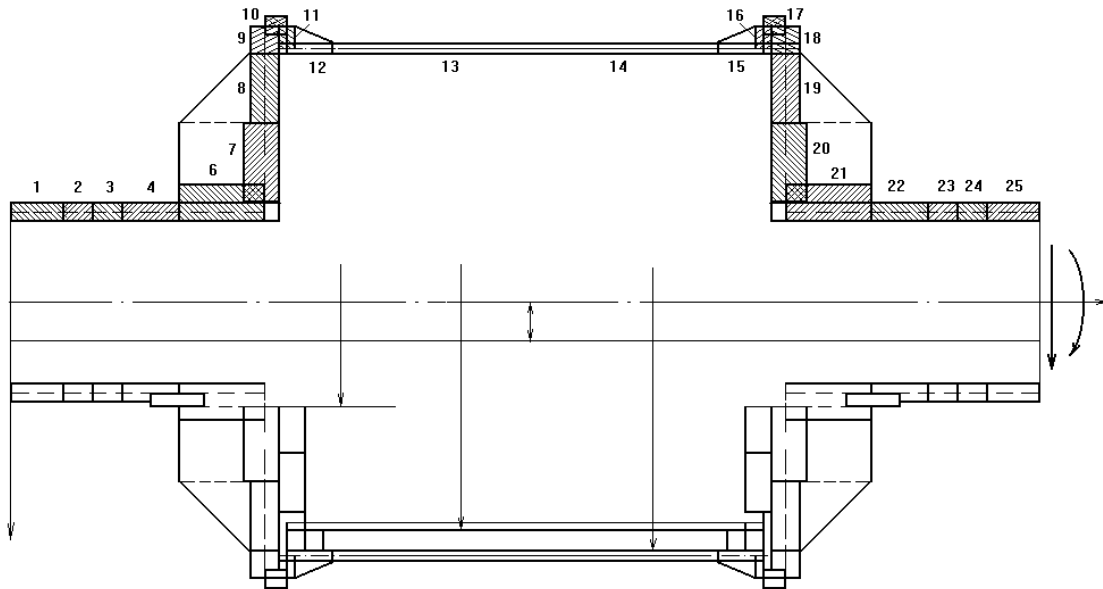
Загальний вигляд барабана рудорозмельного млина
